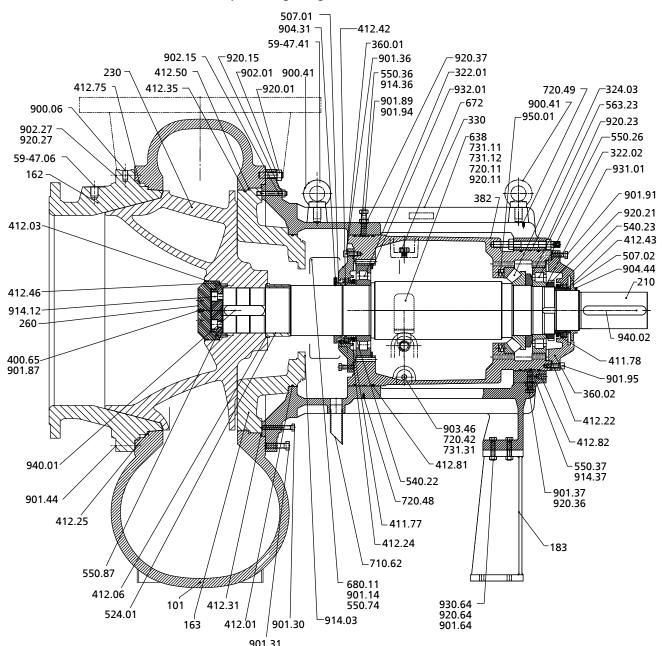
Gesamtzeichnung Pumpe mit Lagerträger P20sx V10
